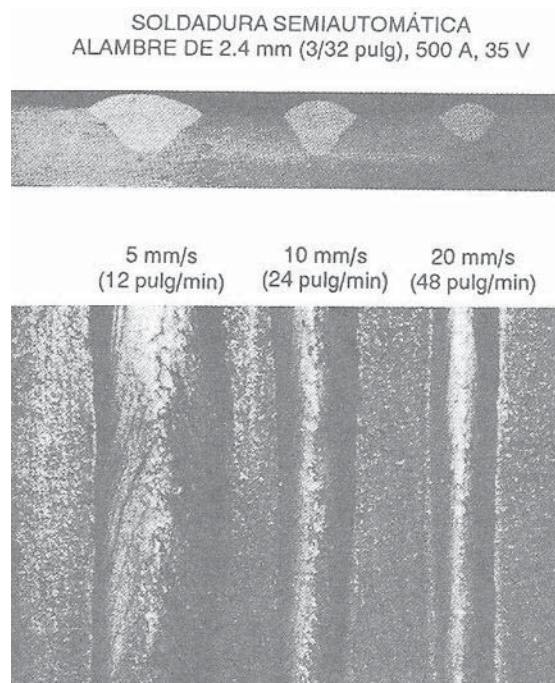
Efecto en la velocidad de desplazamiento sobre la forma y penetración del cordón de soldadura [1].
